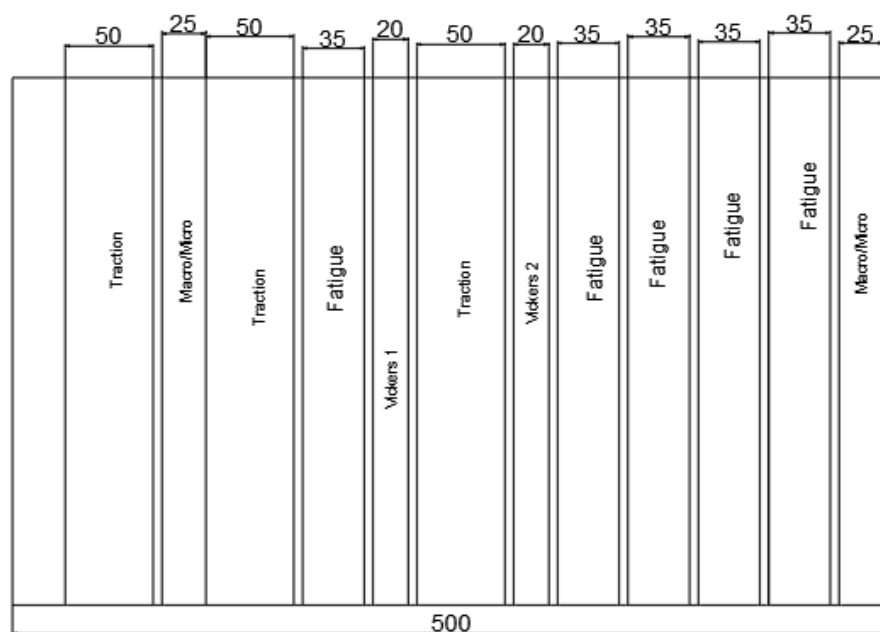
Plan d'usinage pour les tests finaux au centre de l'extrusion (dimensions en mm)
